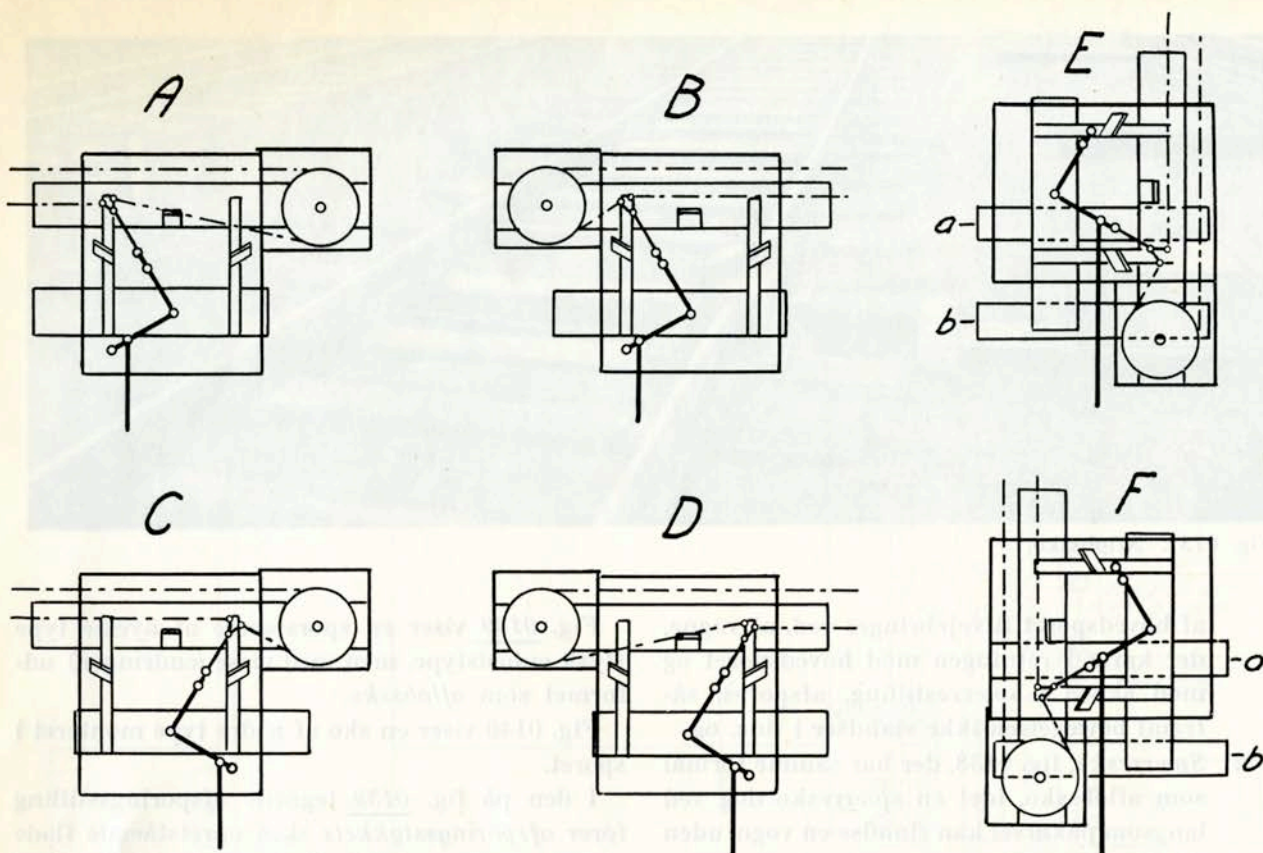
Sporskiftedrev af enhedstypen. Eksempler på sammenskrugging af drevets enkelte dele.
